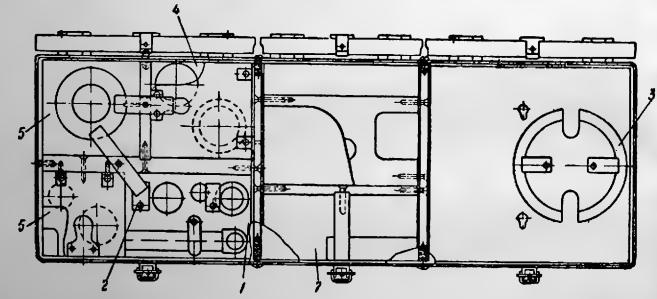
Унифицированный ящик орудийного ЗИП: 1 — колодка под стойку прицела (3-42); 2 — крышка (3-41); 3 — колодка обтюрационного кольца (3-40); 4 — колодка ударного механизма (3-38); 5 — колодка под протирку (3-32); 6 — колодка под банку жидкой смазки (3-29); 7 — колодка под фонарь (3-24); 8 — схема укладки ЗИП (3-17); 9, 10 — заклепки (А510071-7)
